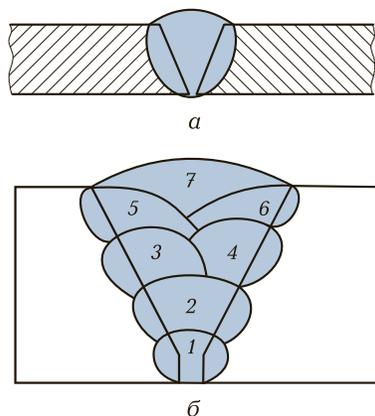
Однослойный (а) и многослойный (б) сварные швы:
